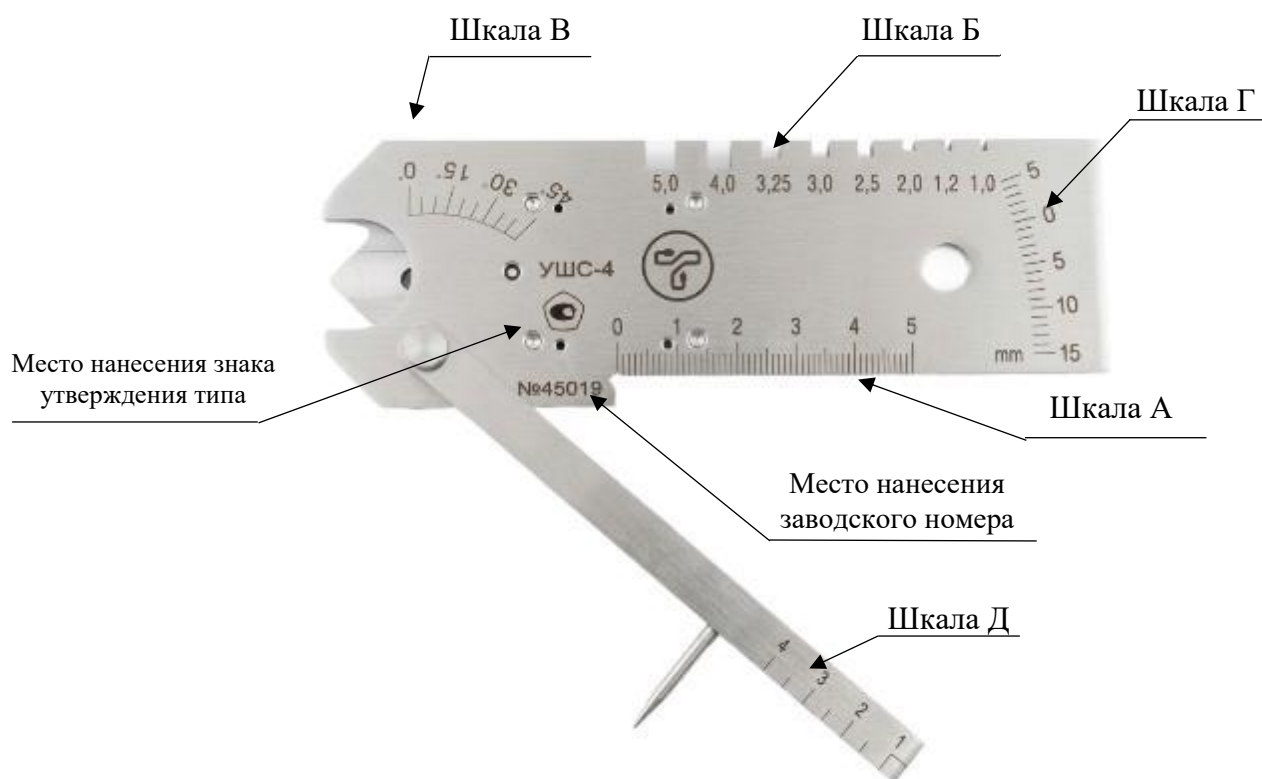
Общий вид шаблона сварщика универсального УШС-4
